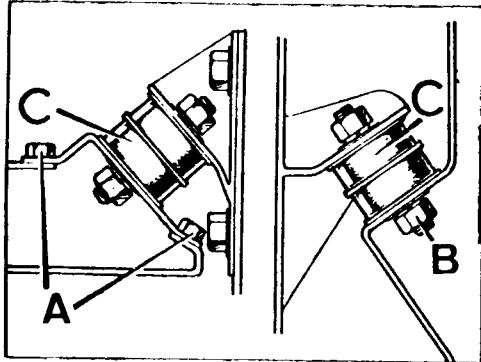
Desmontaje de los tacos de apoyo del motor
